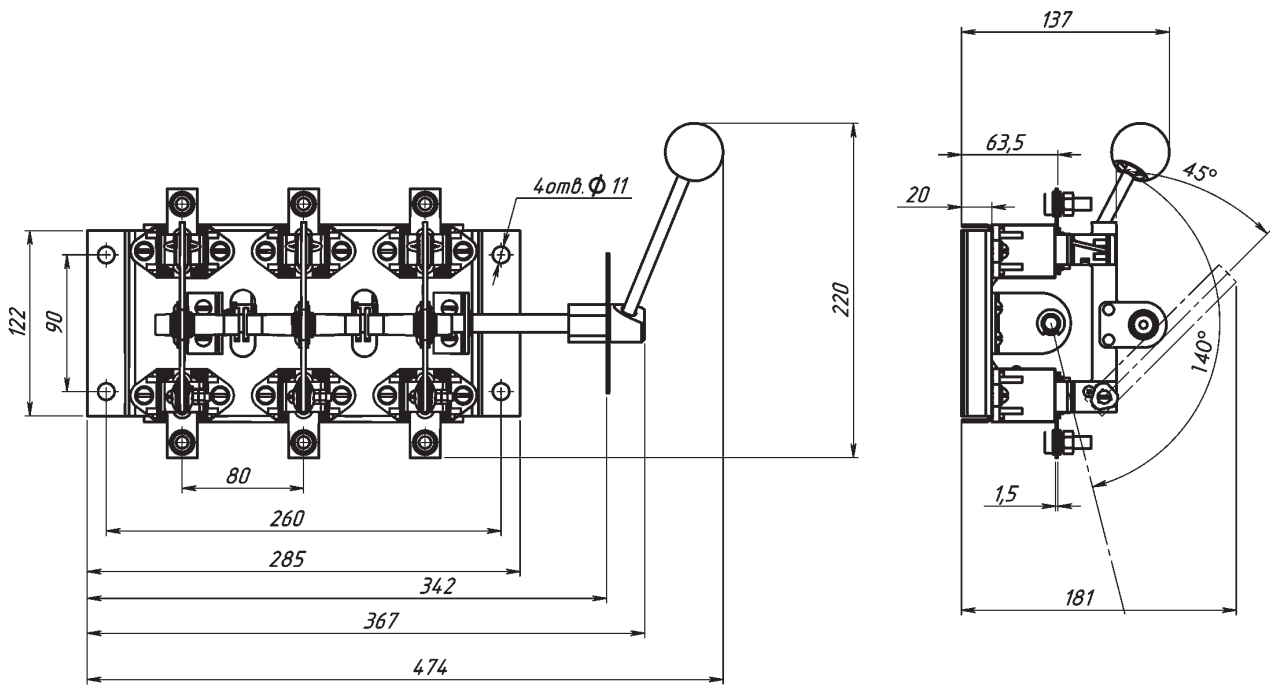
Разъединитель серии Р с боковой ручкой РБ-1, на номинальный ток 100 А,
